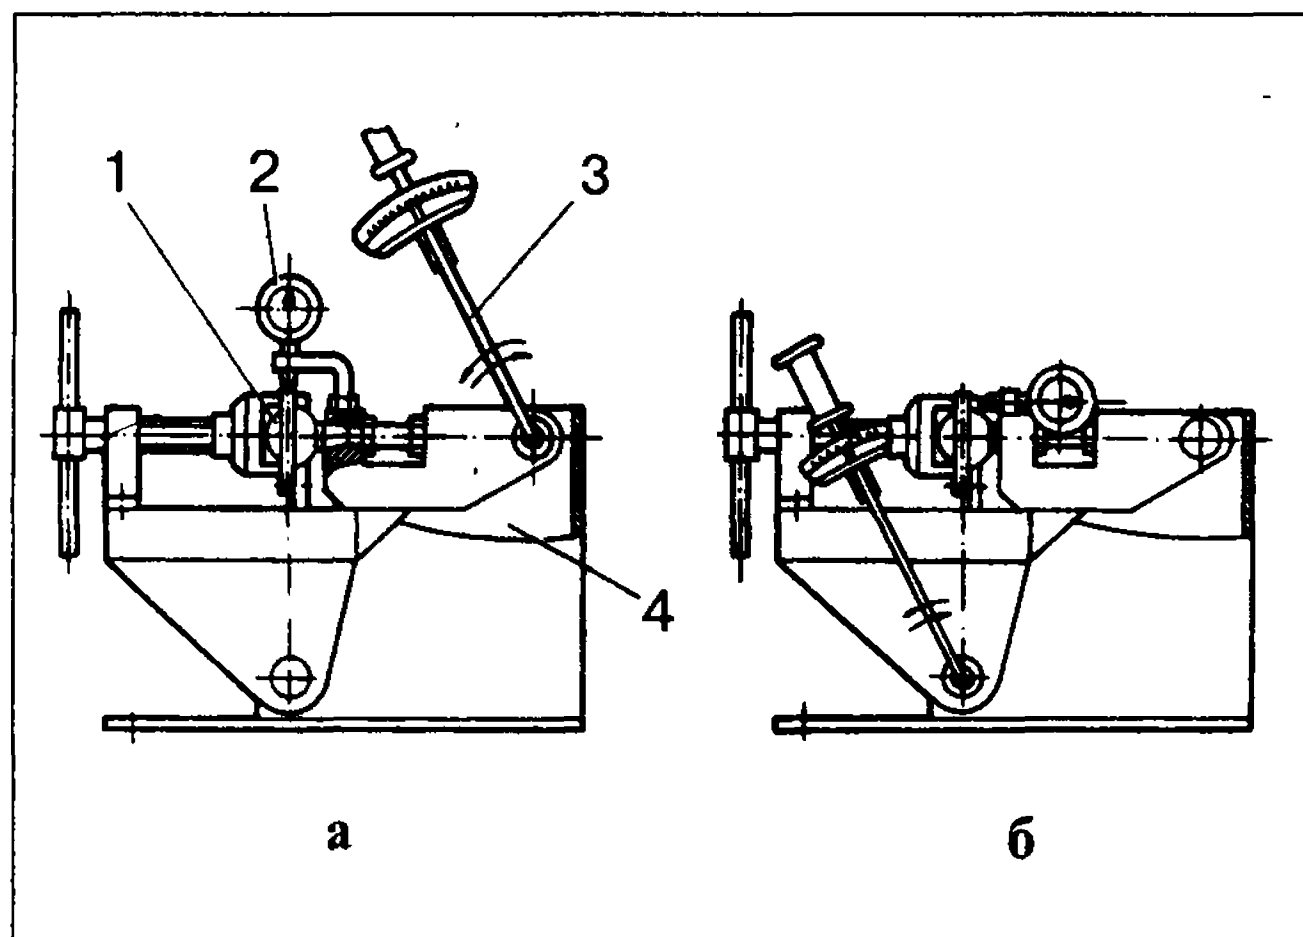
Проверка верхнего шарового шарнира на приспособлении 02.8701.9502:
